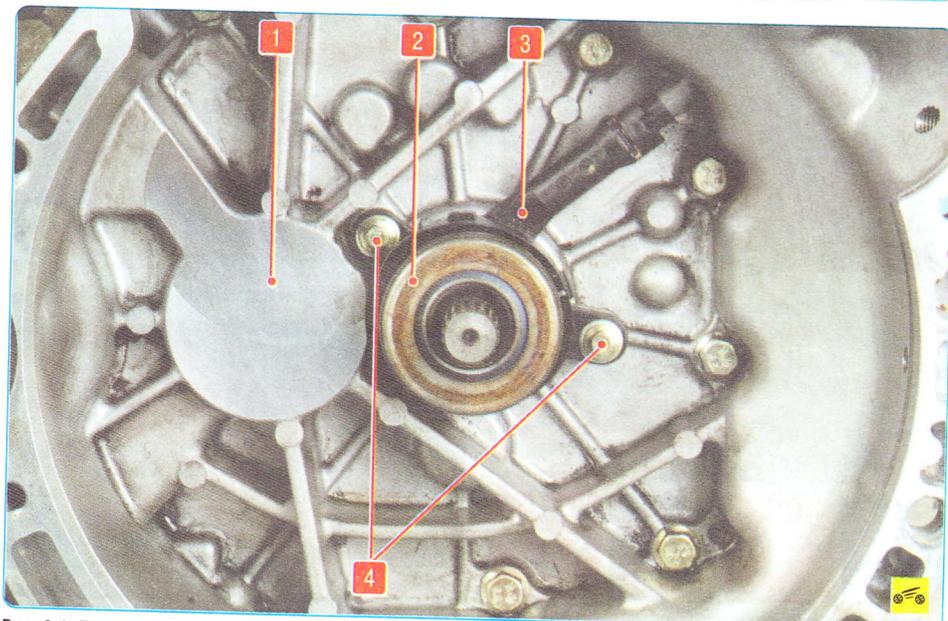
Подшипник выключения сцепления, объединенный с рабочим цилиндром привода выключения сцепления: 1 – картер сцепления; 2 – подшипник выключения сцепления; 3 – рабочий цилиндр привода выключения сцепления; 4 – болты крепления рабочего цилиндра привода выключения сцепления
